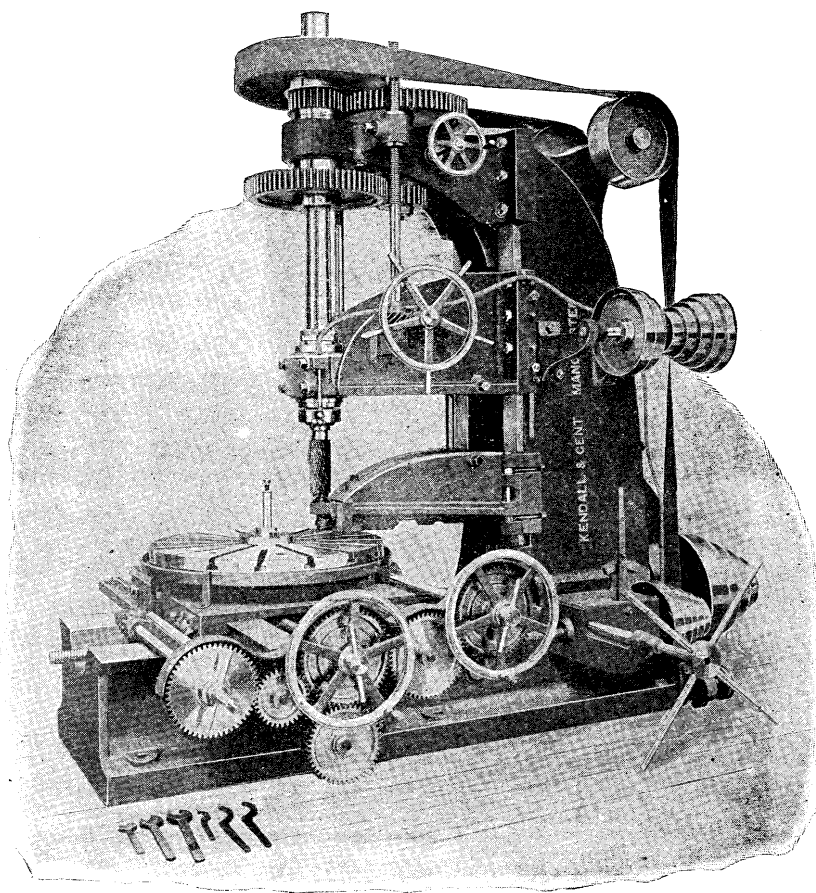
Fraiseuse verticale de MM. Kendall and Gent, de Manchester.
